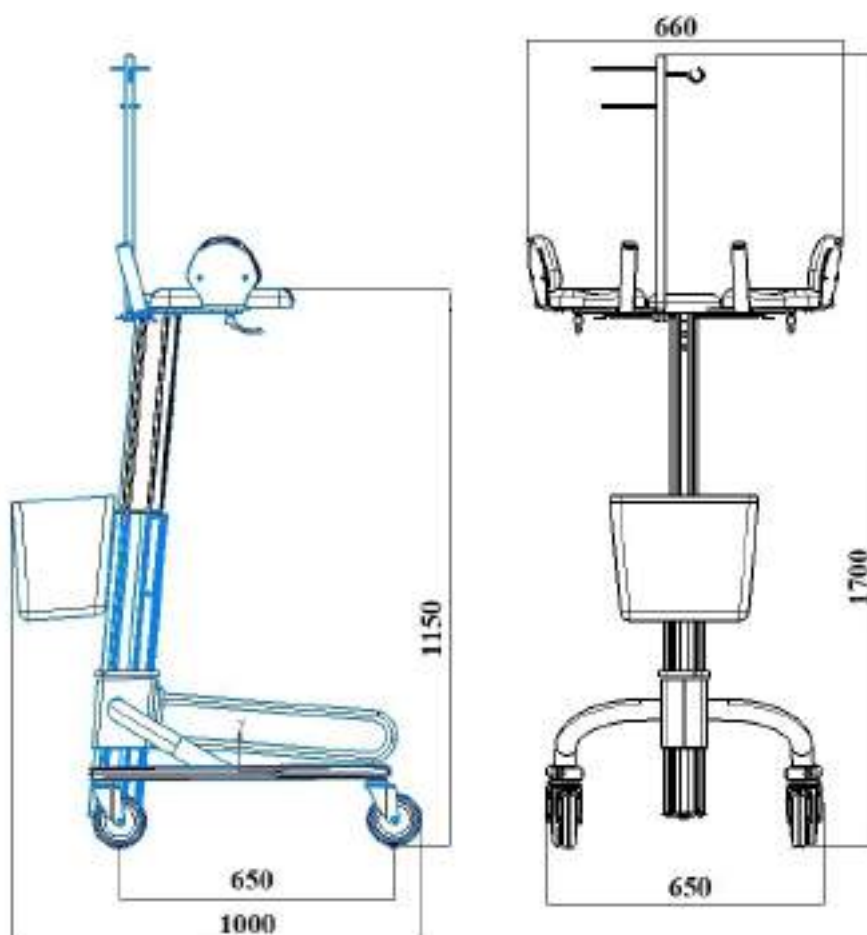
Внешний вид и габаритные размеры Тренажера для ходьбы «ORMED LIFT LM050».
